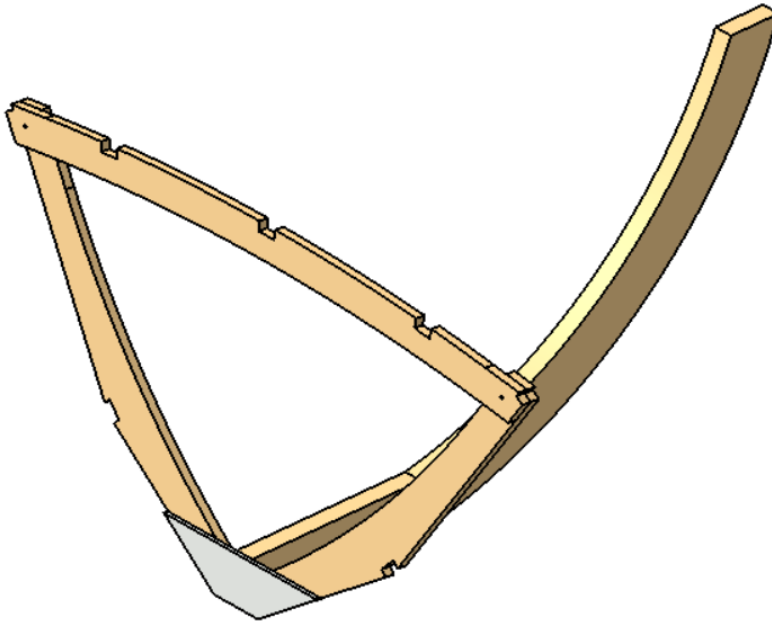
Ensamblaje roda + cuaderna 5. Fuente: propia
